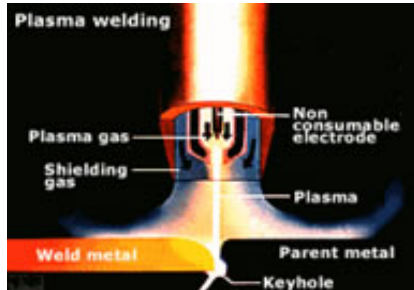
Soldadura por arco plasma empleando la modalidad "Keyhole" durante el proceso, y detalle de la penetración pasante mediante este método de soldadura.
